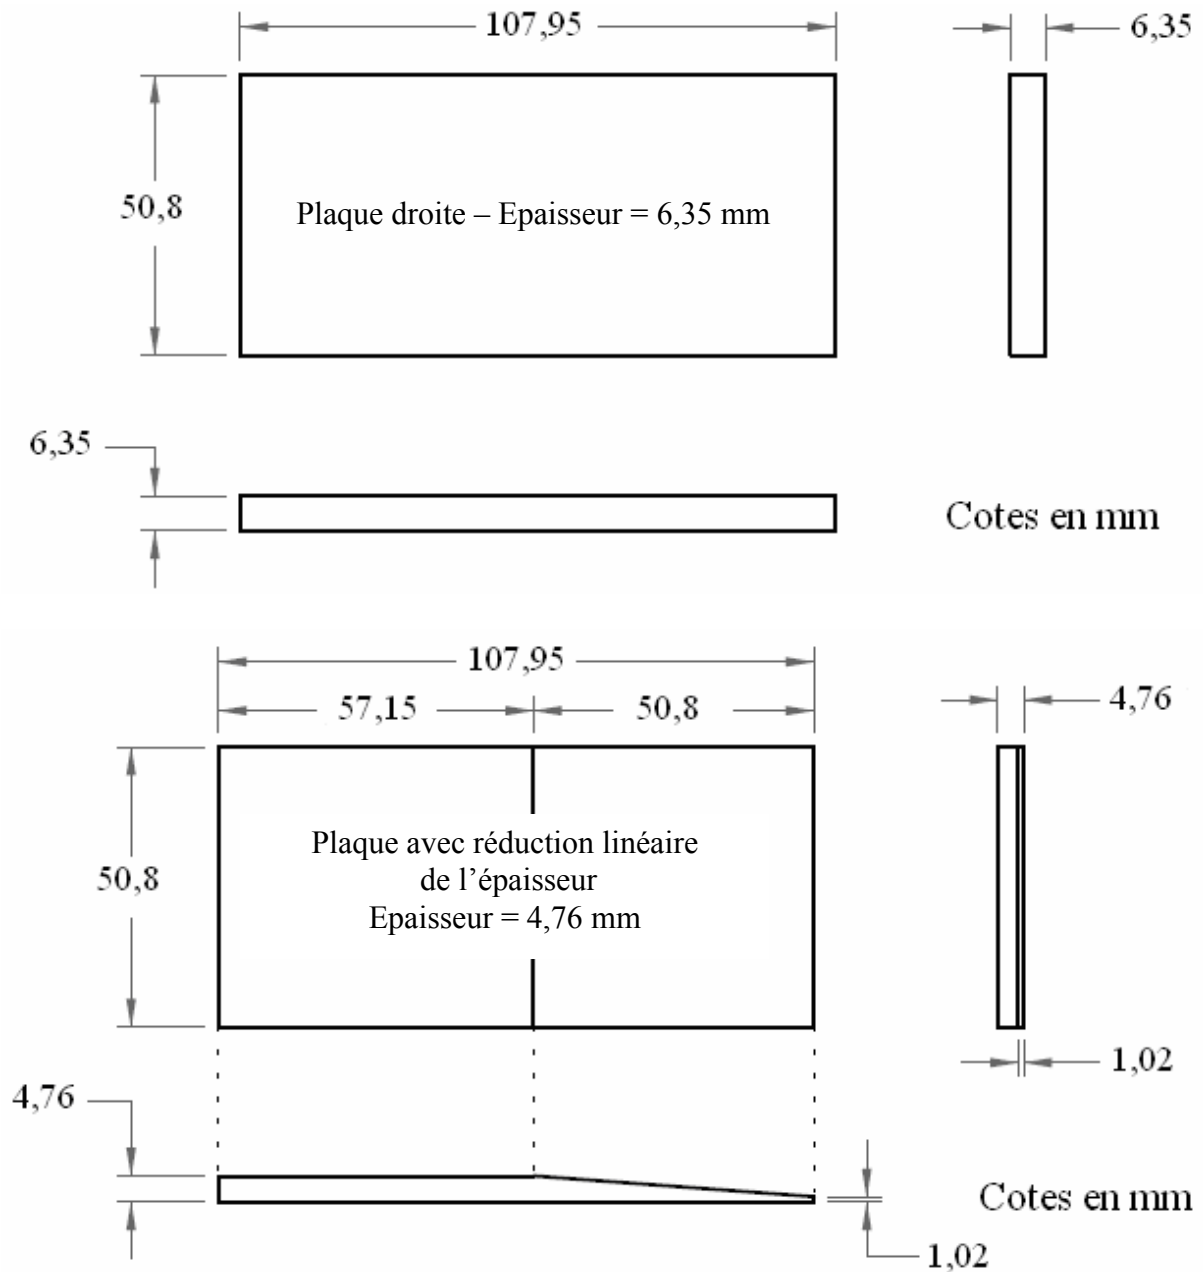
Plans des plaques d'aluminium (AU4G) utilisées pour les essais de traction directe
